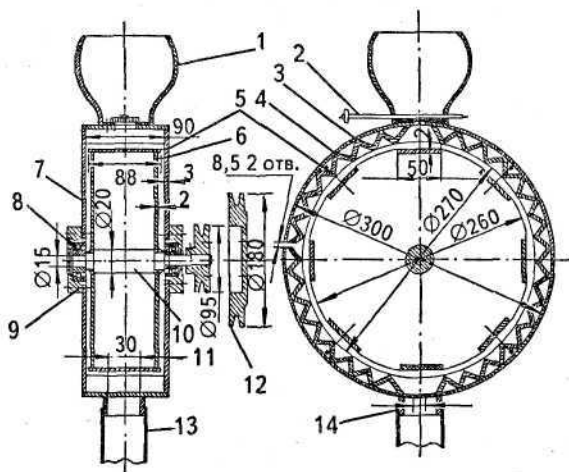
Устройство мельницы-дробилки (первый вариант): 1 — загрузочный бункер-чугунок; 2 — задвижка; 3 — обечайка; 4 — угольник — 20×20×90; 5 — полоса — 2×50×88; 6 — диск; 7 — крышка боковая; 8 — шарикоподшипник № 202; 9 — корпус подшипника; 10 — вал; 11 — шкив диаметром 95 мм; 12 — шкив диаметром 190 мм; 13 — рукав дерматиновый; 14 — патрубок
